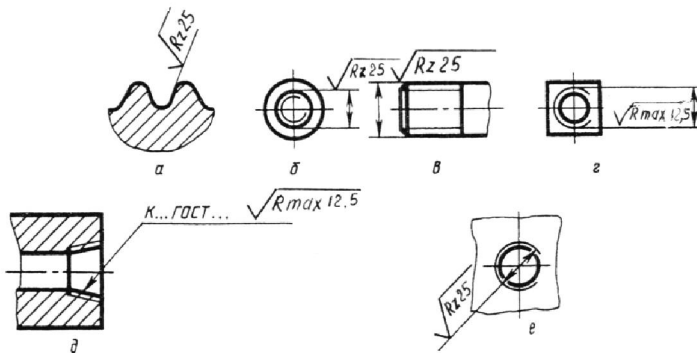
Обозначение шероховатости поверхности профиля резьбы
